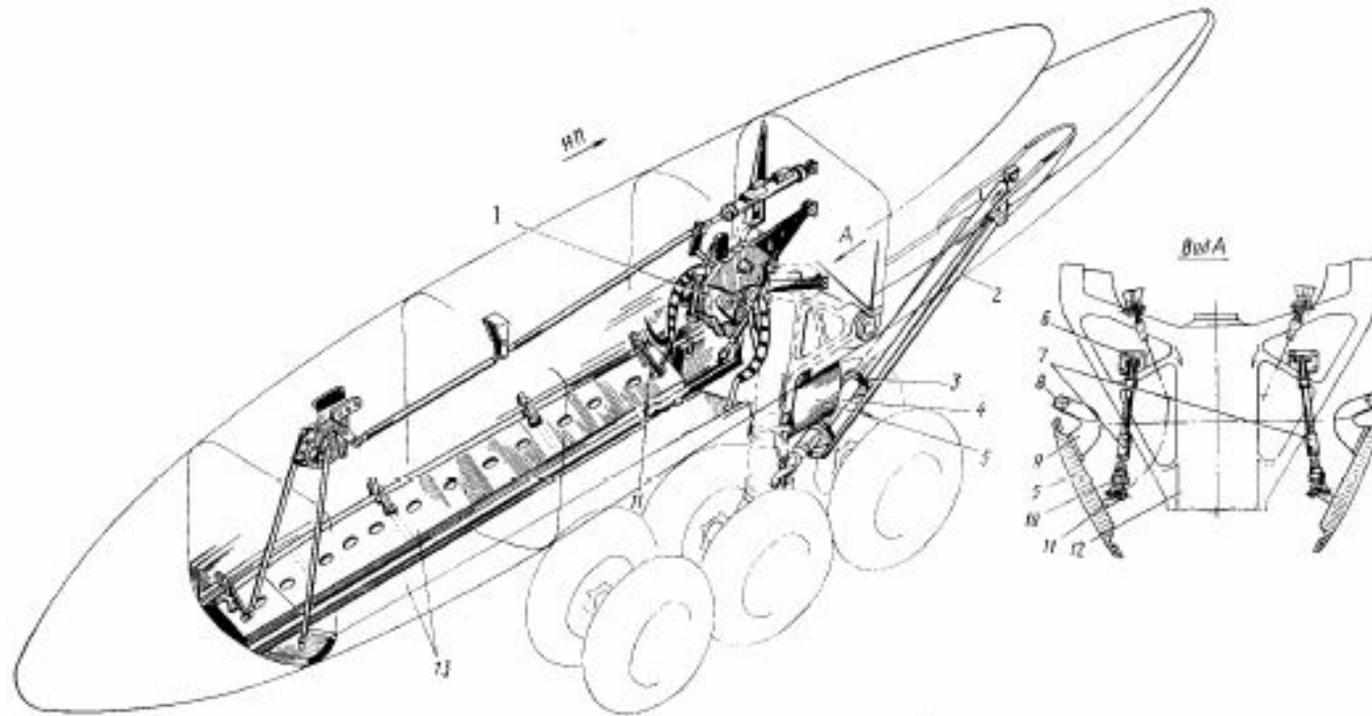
Механизмы управления створками люков главных ног шасси: 1—механизм управления задними створками; 2—щиток; 3, 6, 9, 11—кронштейны; 4—подкос-цилиндр ног шасси; 5—передняя створка; 7—тяга; 8—петля; 10—кардан; 12—траверсы; 13—задние створки.
